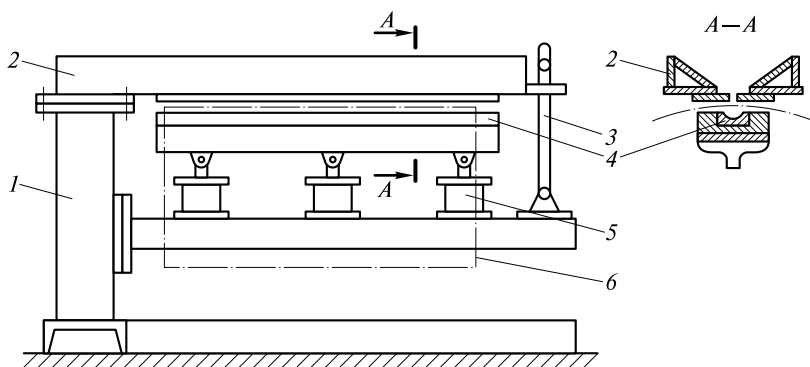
Стелд для сварки продольных швов обечайек:
